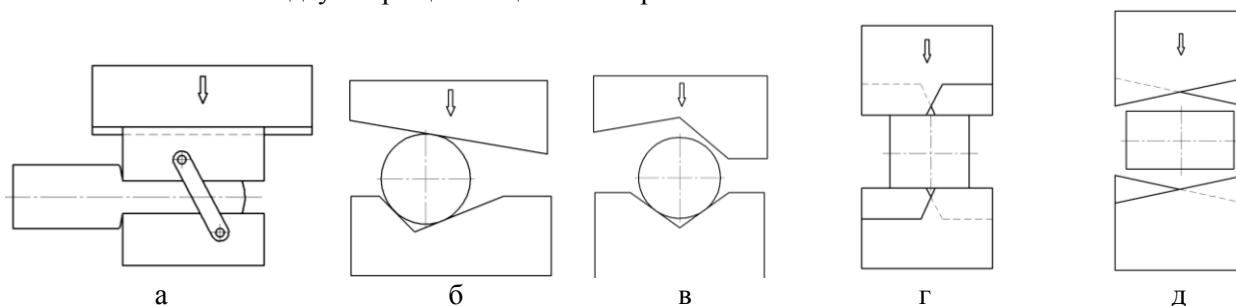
Схемы, обеспечивающие дополнительный макросдвиг в заготовке при протяжке
